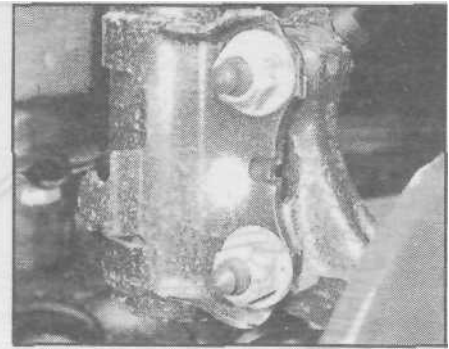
Гайки/болты крепления стойки к поворотному кулаку
